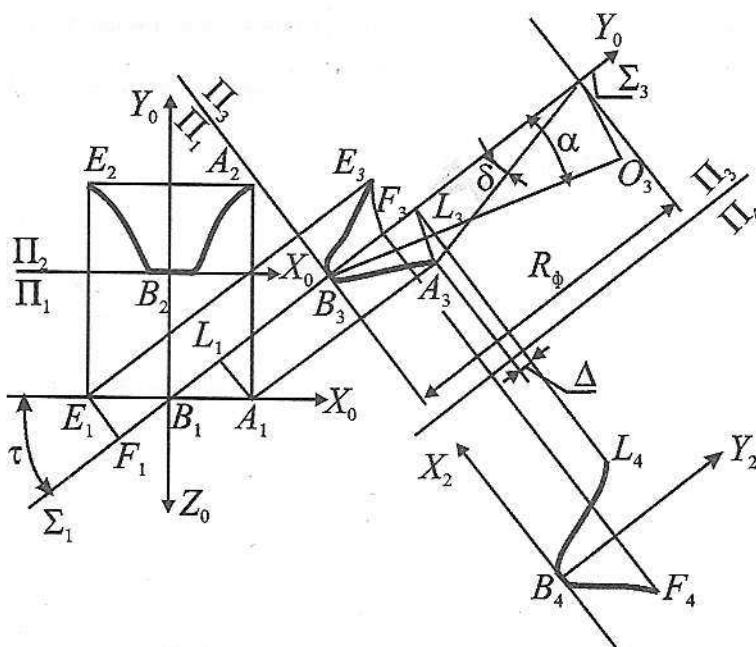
Схема образования задней поверхности обкаточной фрезы
